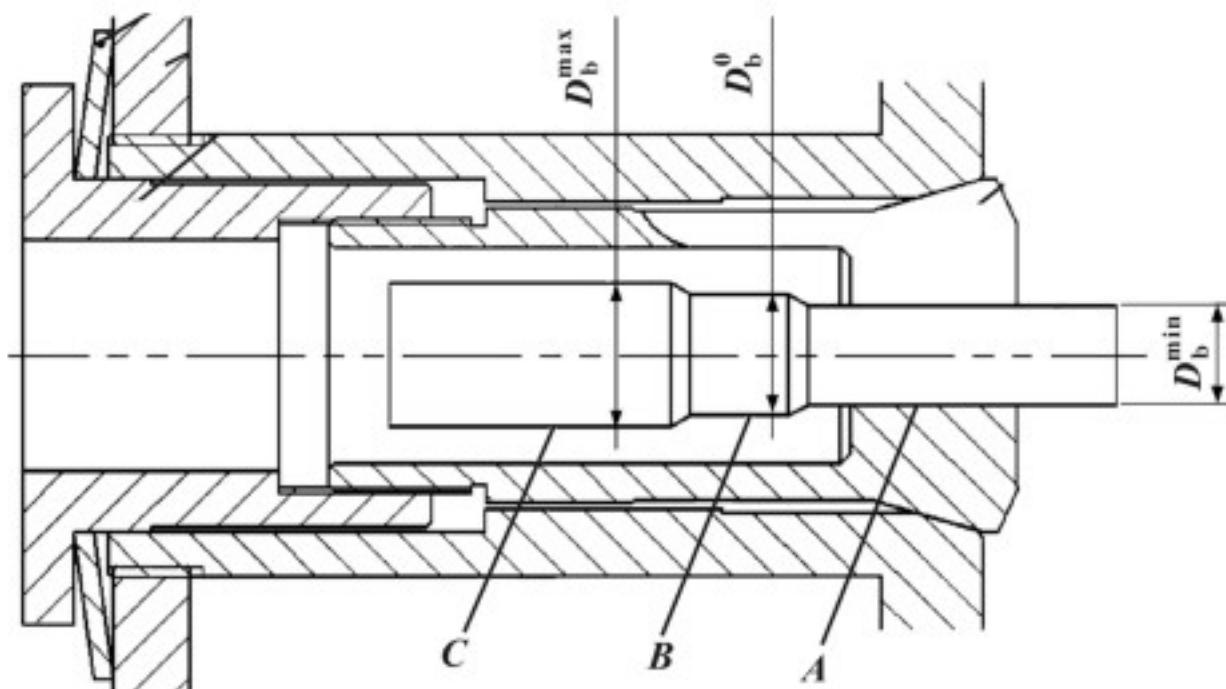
Адаптивна синхронна поворотна напрямна конструкція втулки-пружини цангового стрижня
